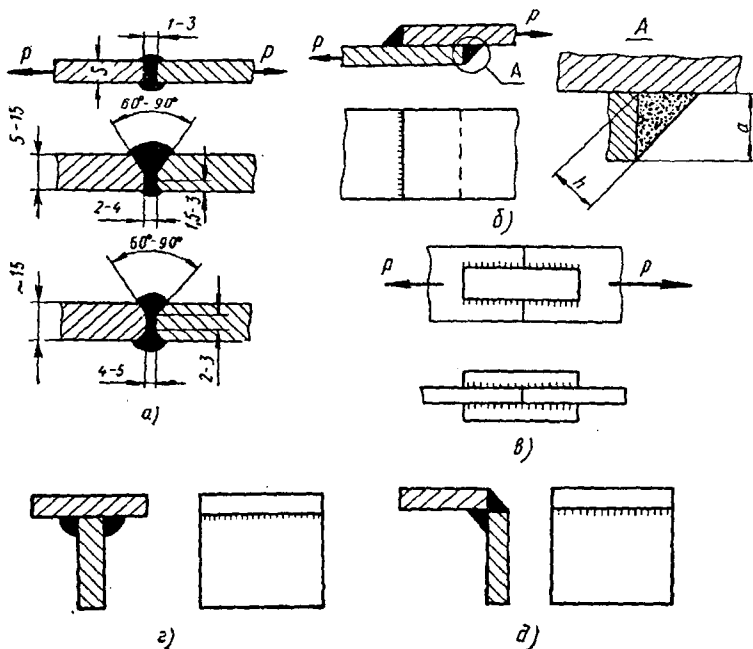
Сварные соединения: а - стык; б - внахлестку; в - с накладками; г - в тавр; д - в угол.
